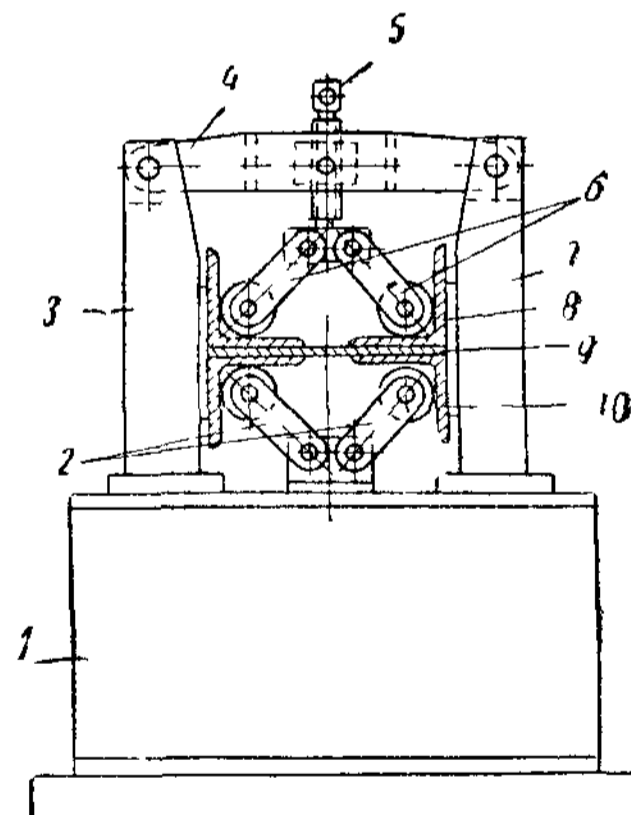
Кондуктор для бездырной сборки элементов Н-образного сечения клепаных конструкций
